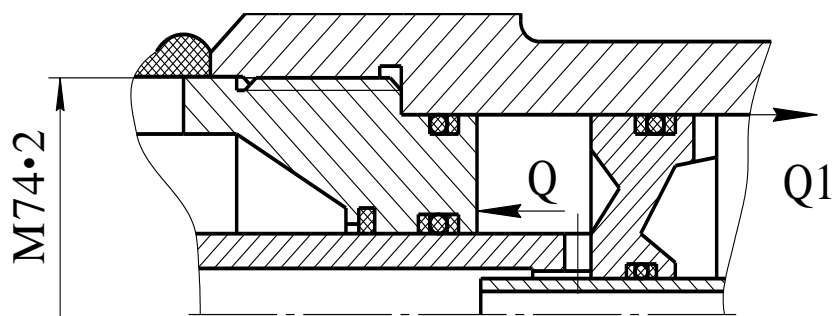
Резьбовое соединение вилки ножей с корпусом гидроблока
